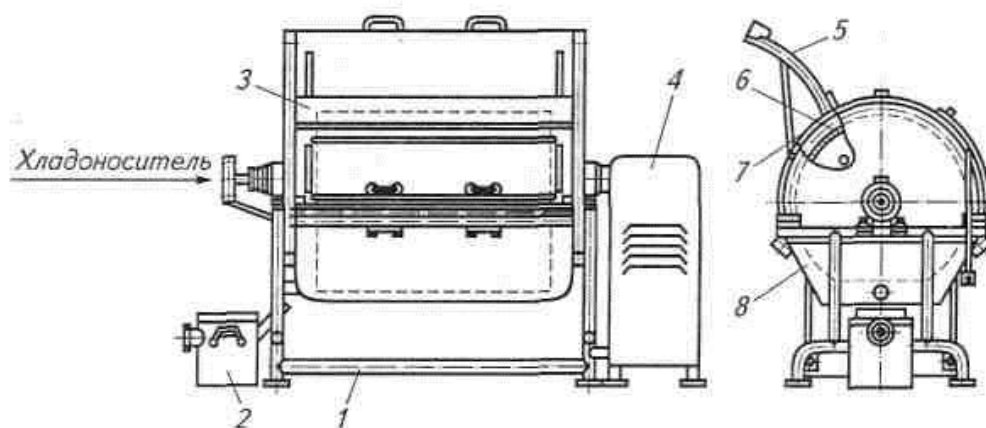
Установка для охлаждения и прессования творога в мешочках: 7 — рама; 2—отстойник; 3 — кожух; 4— привод; 5 — дверца; 6 — трубчатый барабан; 7— загрузочное окно; 8 — ванна
